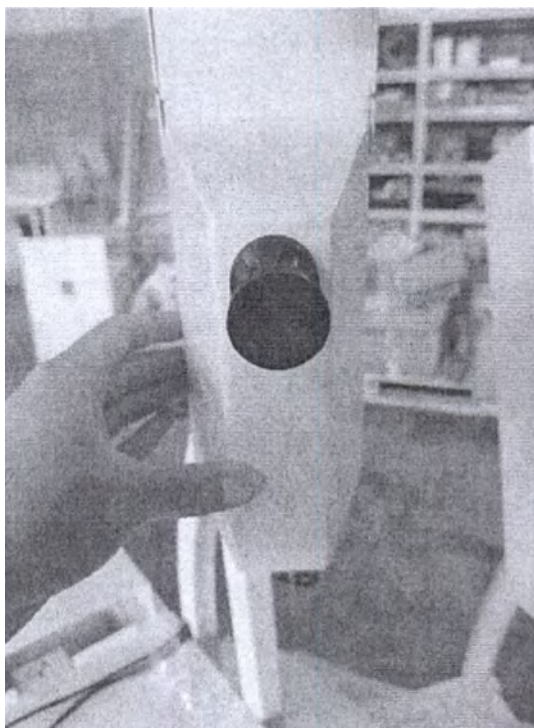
Закрепление декоративной крышки алкотестера
